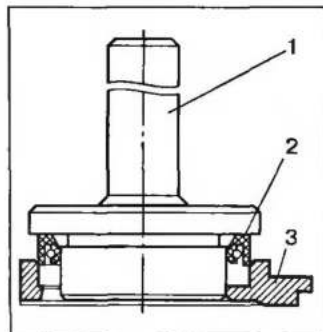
Запрессовка сальника в держатель (крышку) заднего подшипника коленчатого вала: 1 — оправка; 2 — манжета; 3 — держатель
